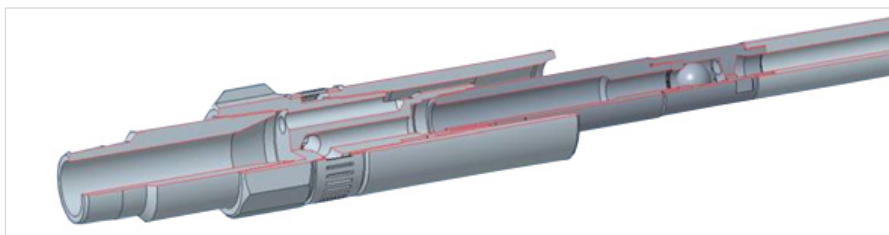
Схема сборки смесителя скважинного СС-89 с жестким резьбовым соединением и держателя седла клапана насоса
